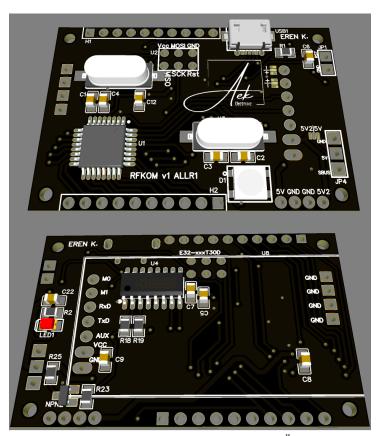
Alıcı Kartı PCB Çizimi (Ön Yüz)
